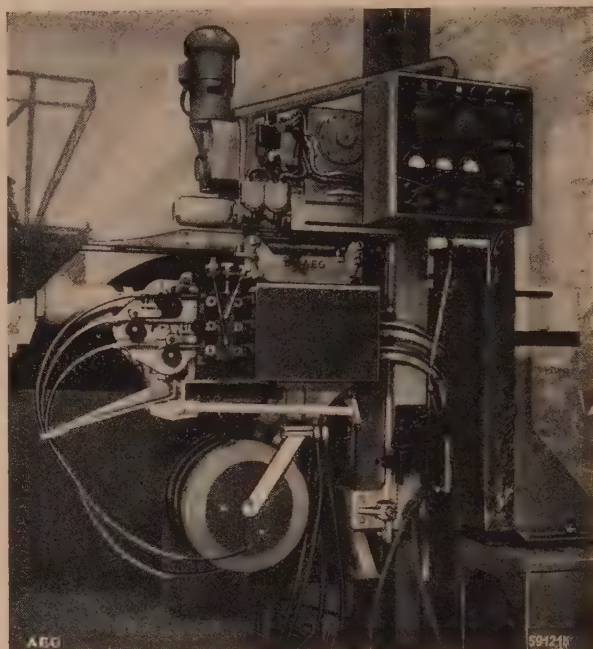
Der Schweißautomat LEA 400 beim Schweißen von 100 mm dickem Stahlblech
